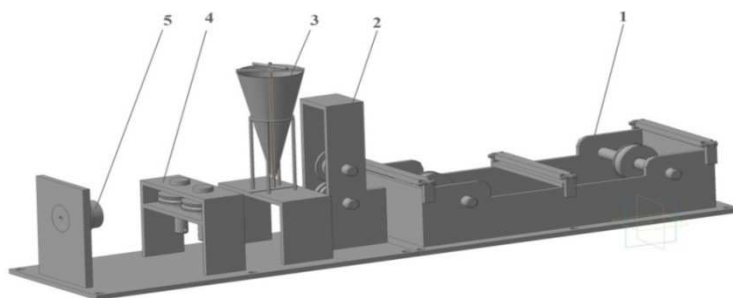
Обобщенная схема установки для изготовления сварочной проволоки:
